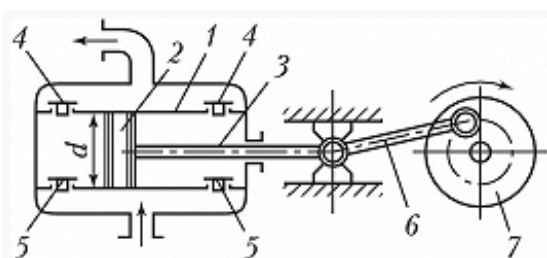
Схема поршневого насоса двустороннего действия: 1 – цилиндрический корпус; 2 – поршень; 3 – приводной шток; 4 – напорный (выпускной) клапан; 5 – всасывающий клапан...
